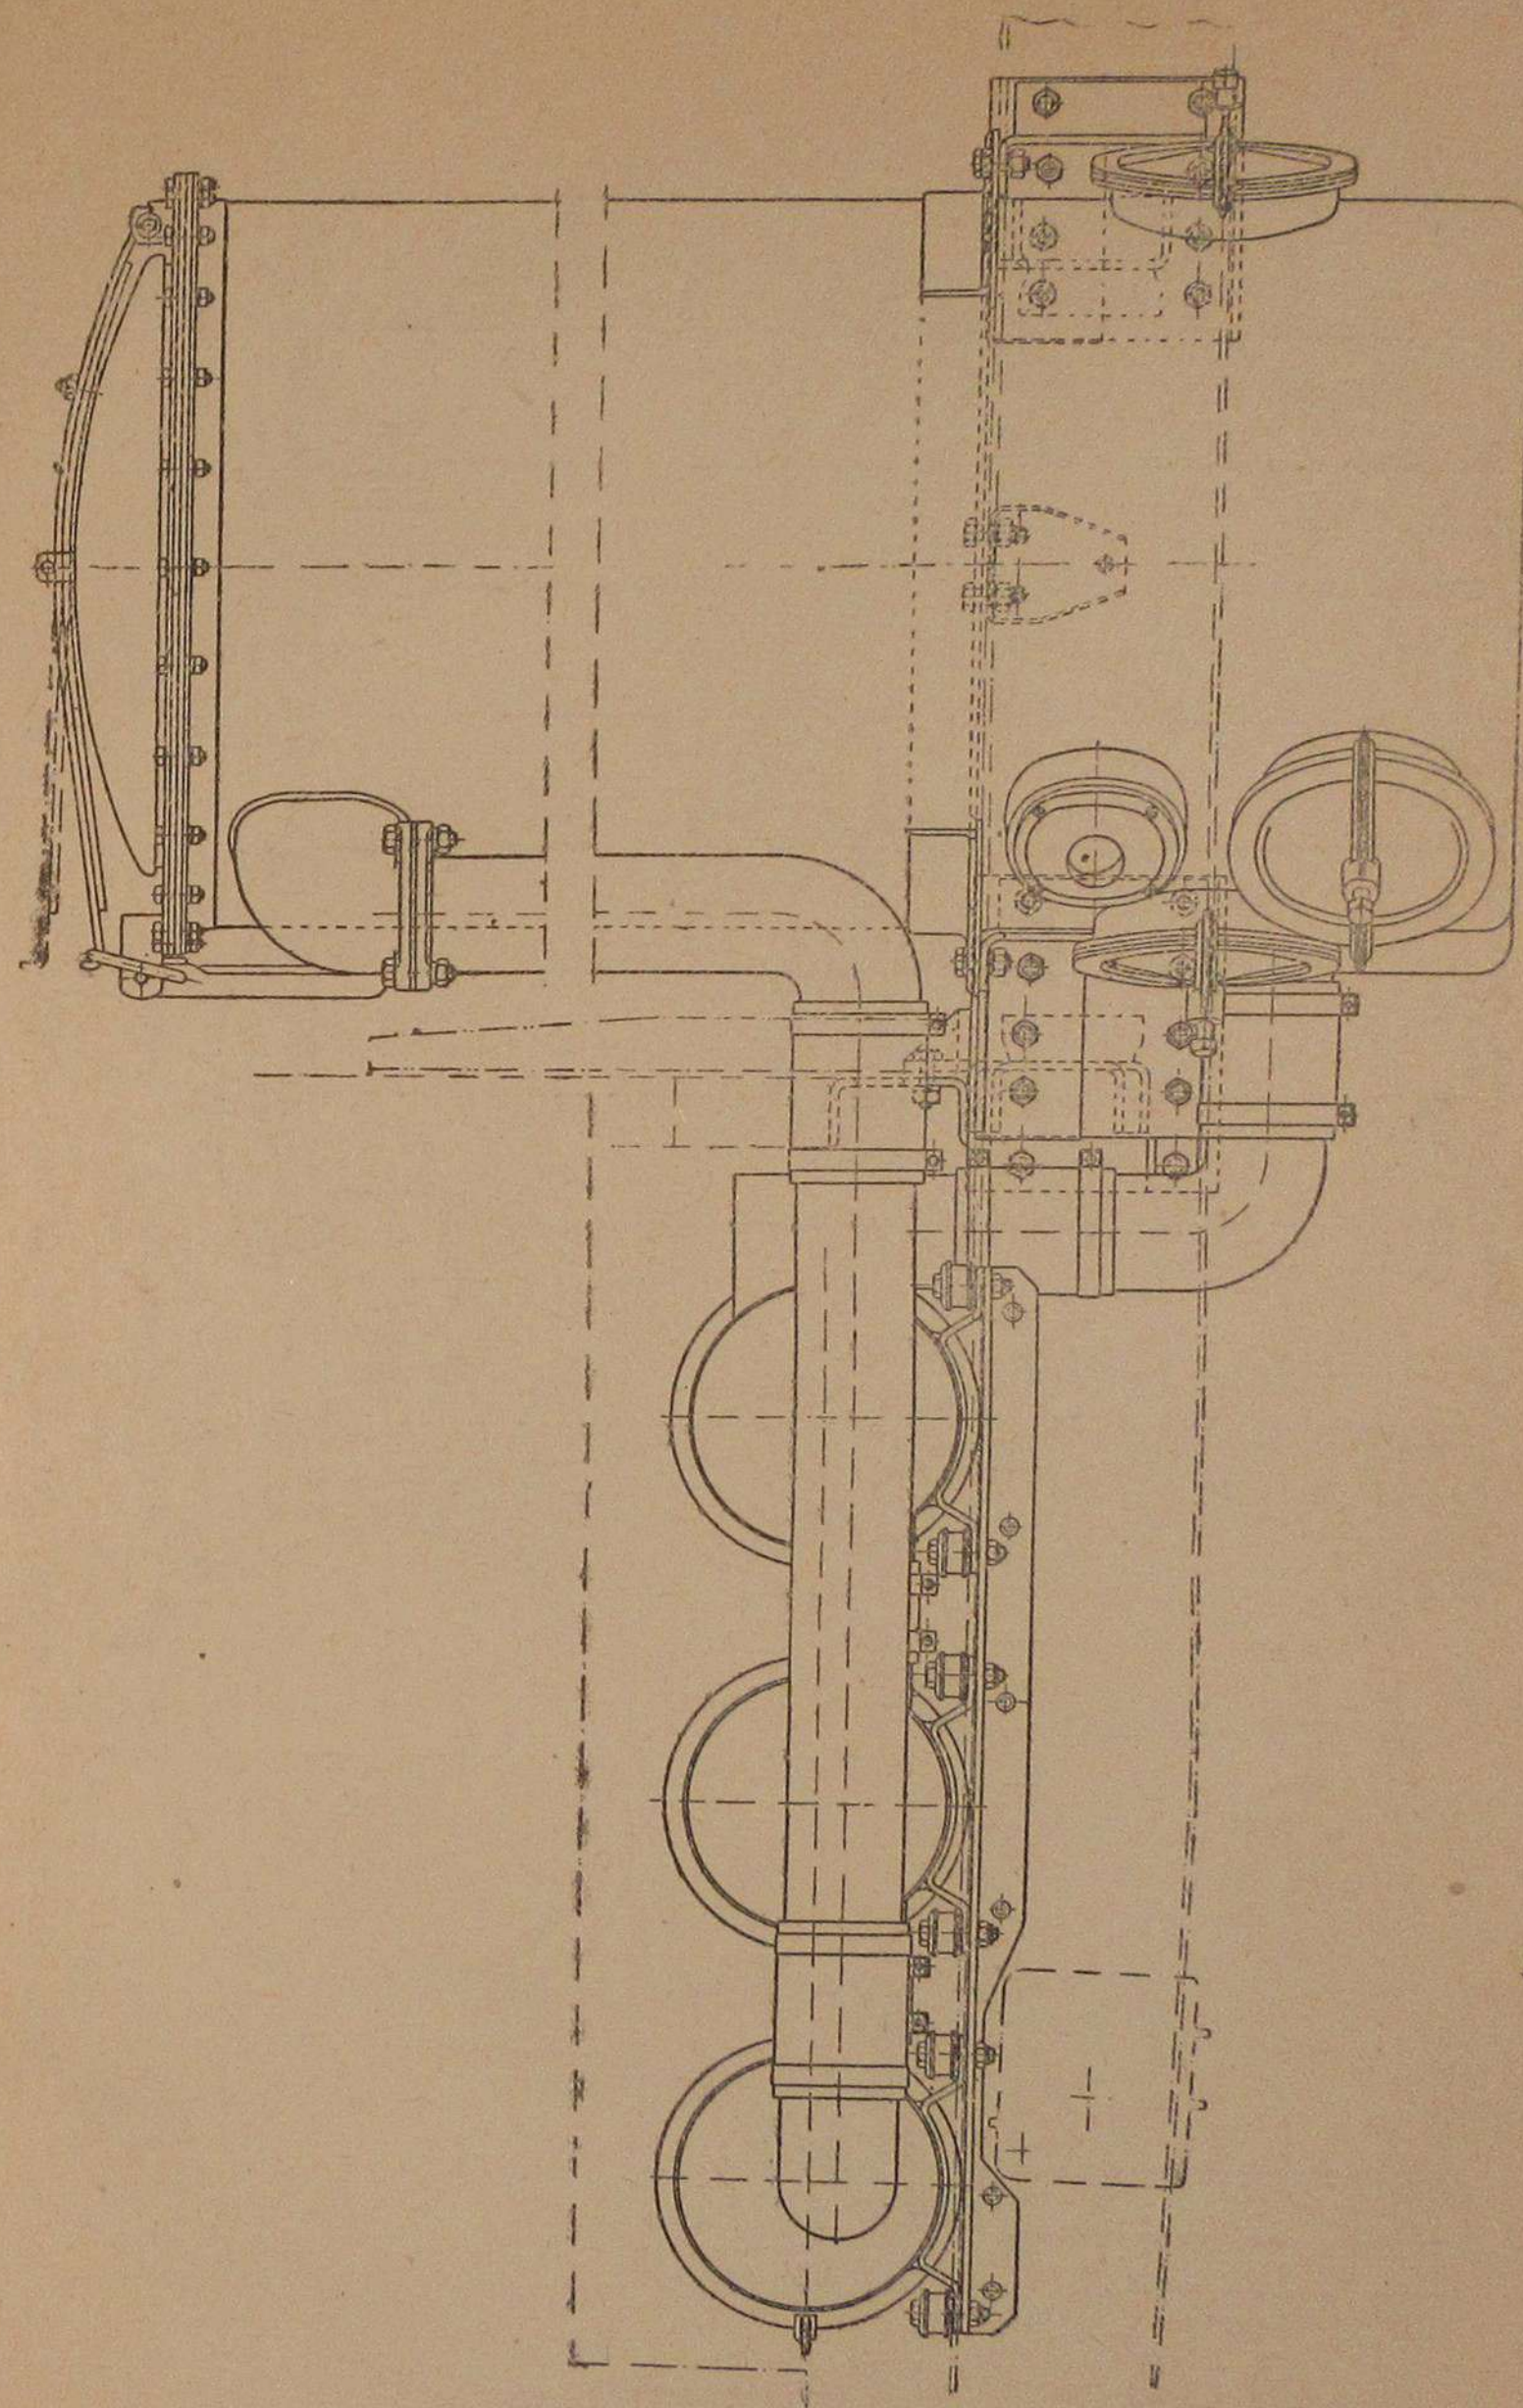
Общий вид сбоку установки и крепления газогенератора ЗИС-21
